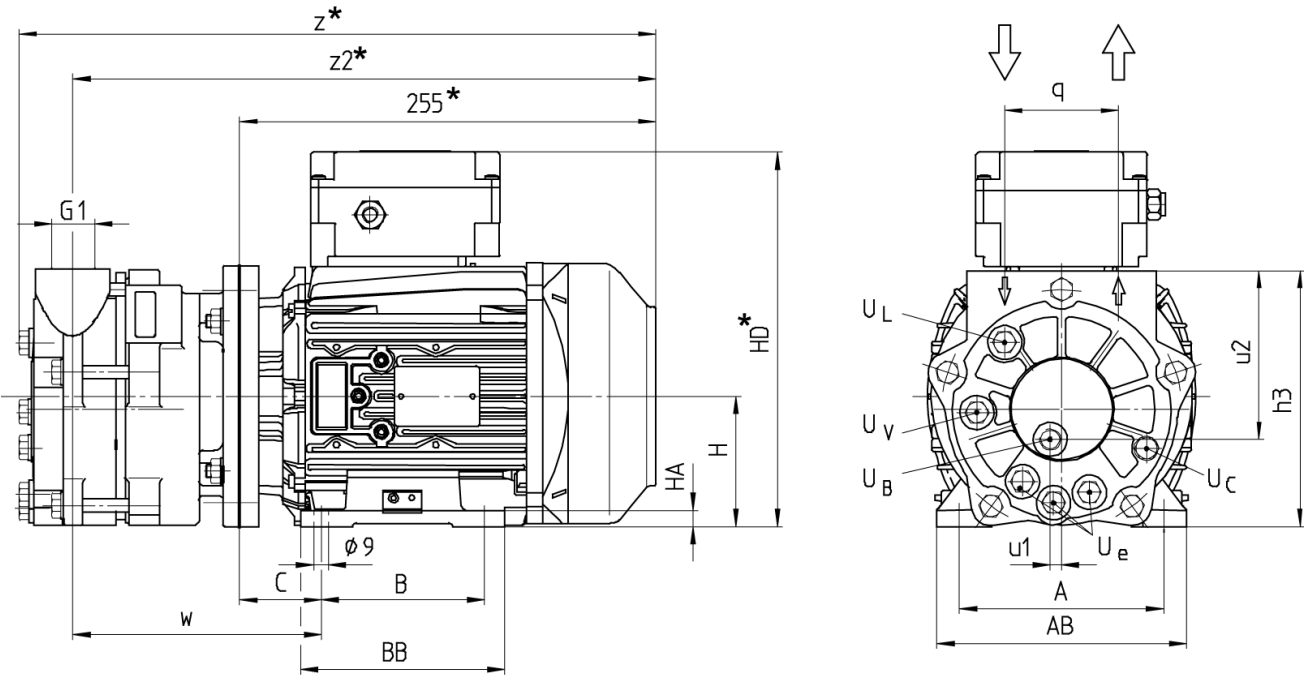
Размерный чертёж LC0030 A/LC0060 A
